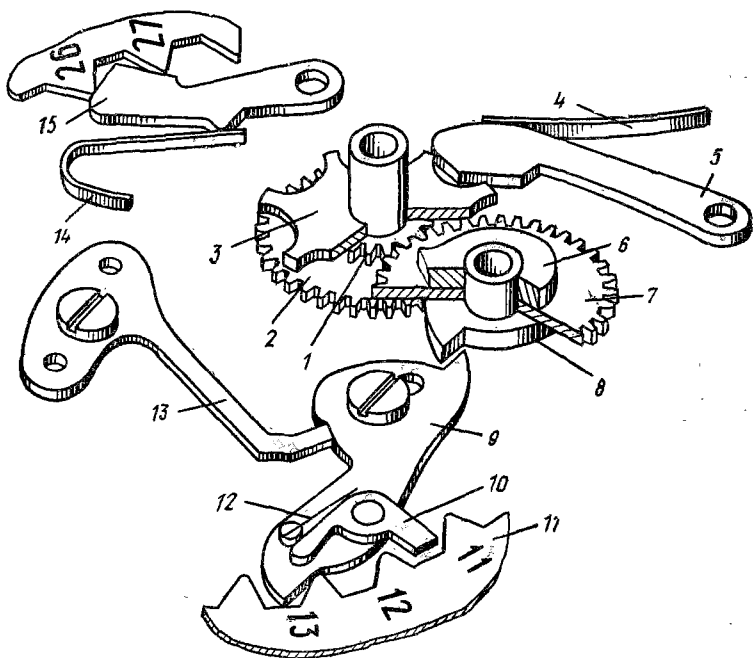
Кинематическая схема календарного устройства часов «Слава» 2427;
